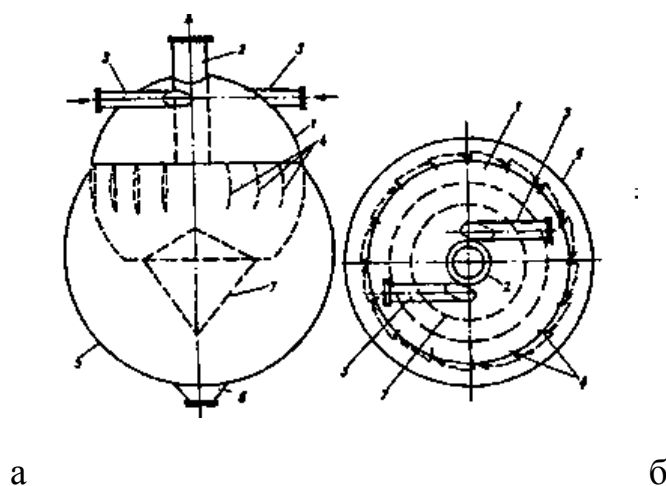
Сферический циклон: а – вид сбоку; б – вид сверху.
